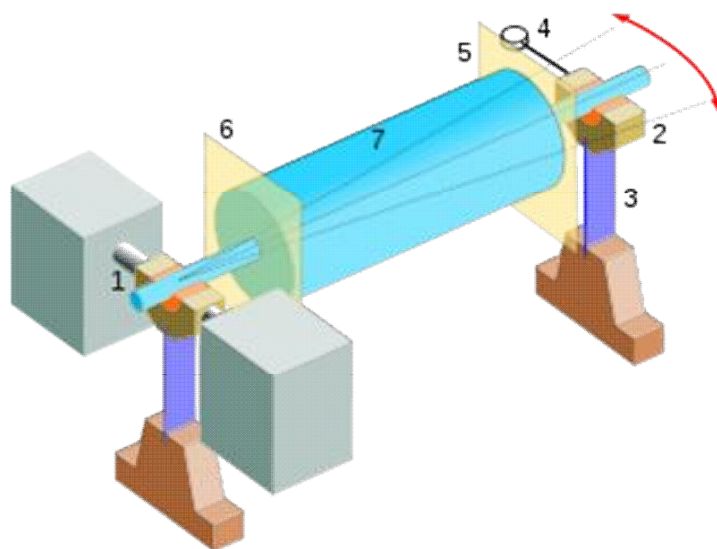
Схема балансувального верстата з пружними опорами: 1 – жорстка опора; 2 – пружна опора; 3 – пружна пластина; 4 – вимірювач коливань; 5, 6 – площини балансування; 7 – ротор.
